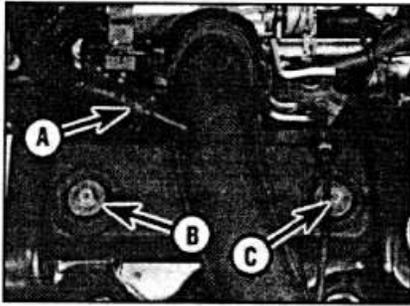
D.6. Расположение дополнительной трубки подачи воздуха в верхней части двигателя (A) и болты крепления (B и C).
